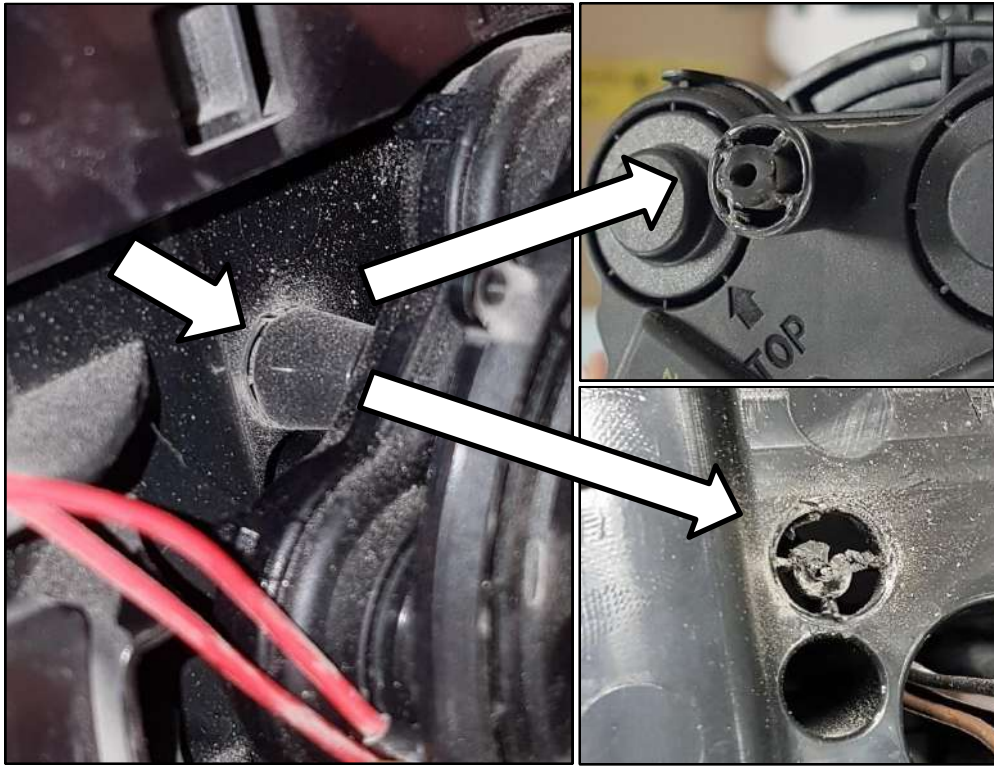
Руйнування кріпильної бобишки моторедуктора
